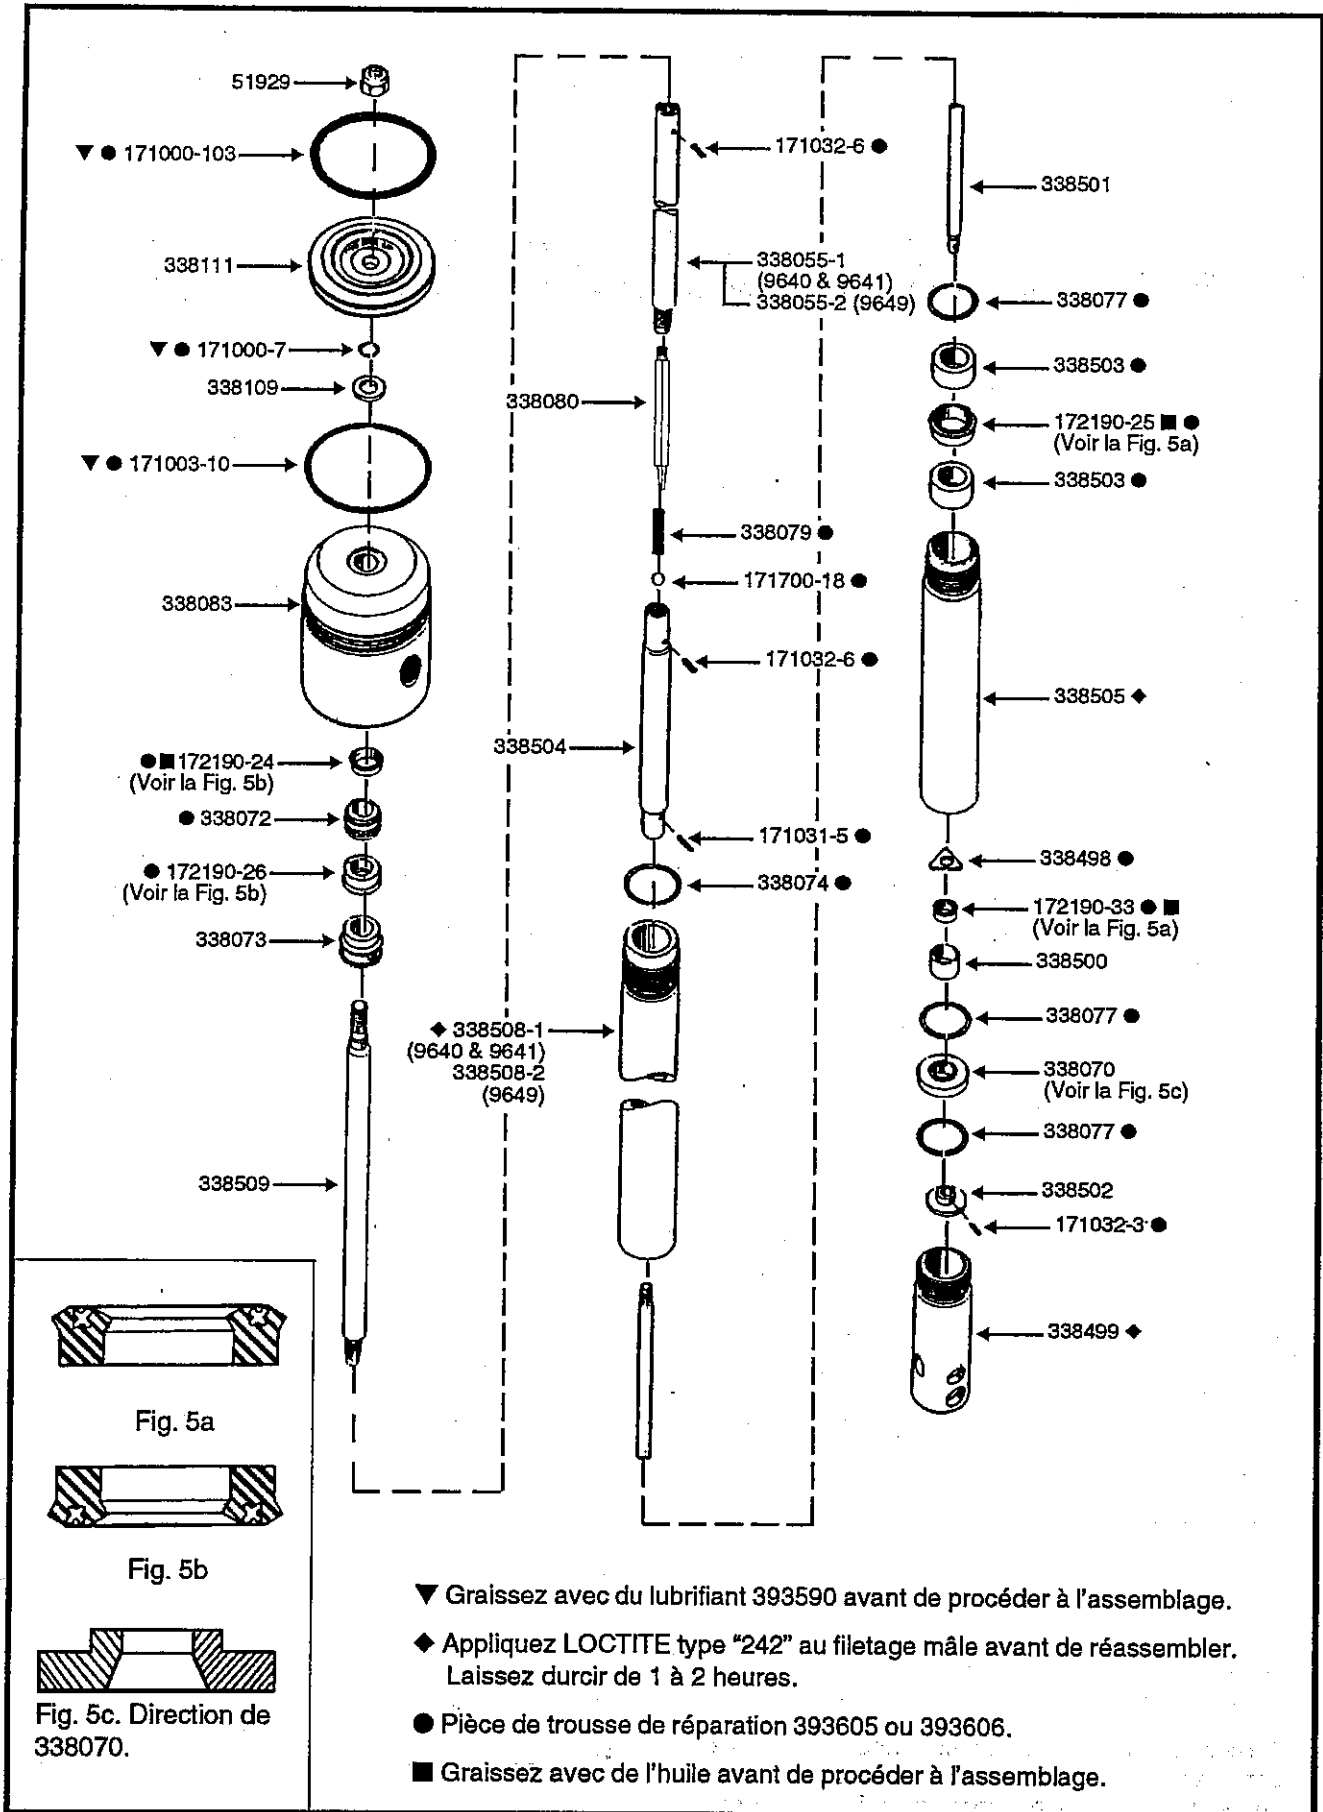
Ensemble de pompe et tube 338497-1 ou 338497-2
